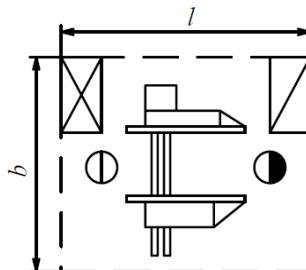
Рабочее место станка Ц2К12Ф-1
